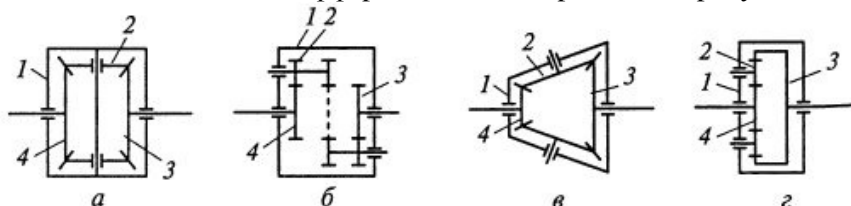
Кинематические схемы шестеренных дифференциалов: а, б - симметричных; в, г - несимметричных; 1 - корпус, 2 - сателлит; 3, 4 - шестерни
